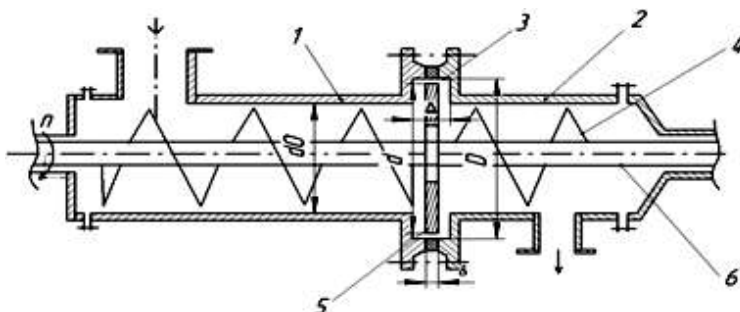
Схема шнекового смесителя с гидрозатвором
